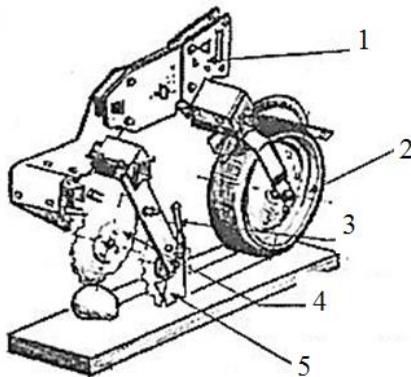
Двухдисковый сошник с прикатывающим катком сеялки компании Pötinger: 1 – корпус сошника; 2 – прикатывающий каток; 3 – семянаправитель; 4 – зубчатый диск; 5 – бороздкообразователь
